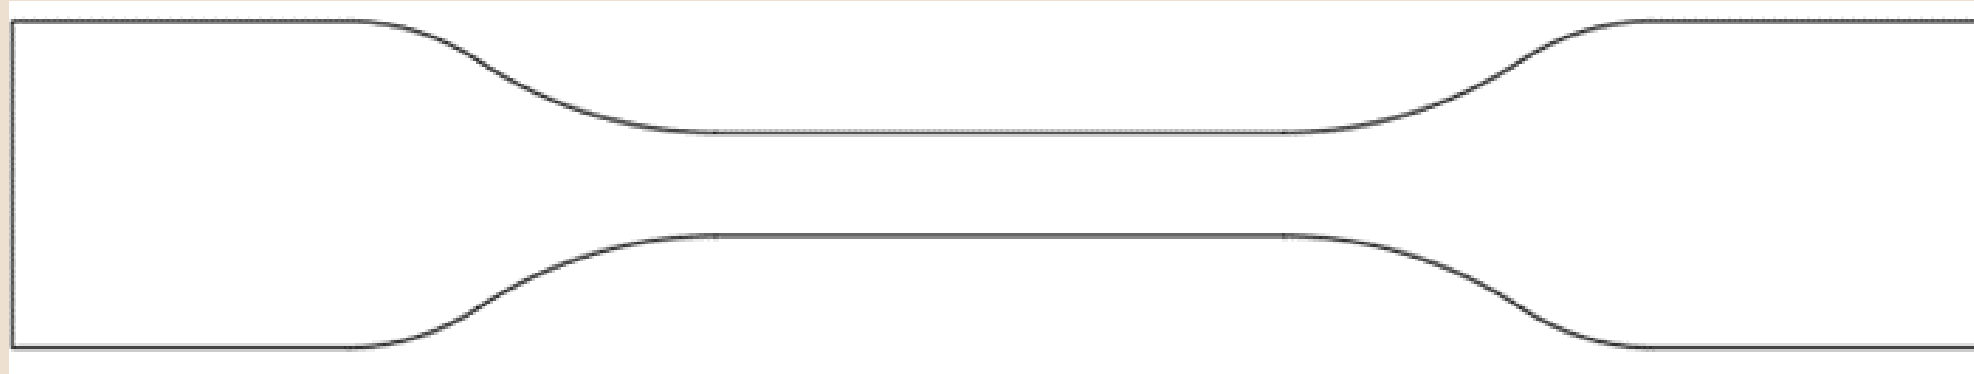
Diseño de probeta. Ilustración del diseño del molde de la probeta.
